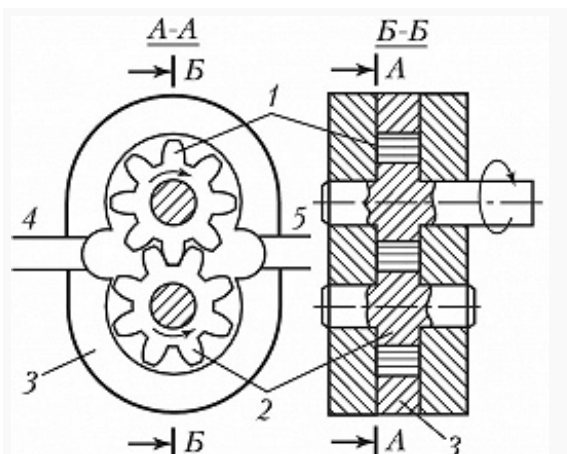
Схема шестерённого насоса: 1 – ведущая шестерня; 2 – ведомая шестерня; 3 – корпус; 4 – всасывающий патрубок; 5 – напорный патрубок.
